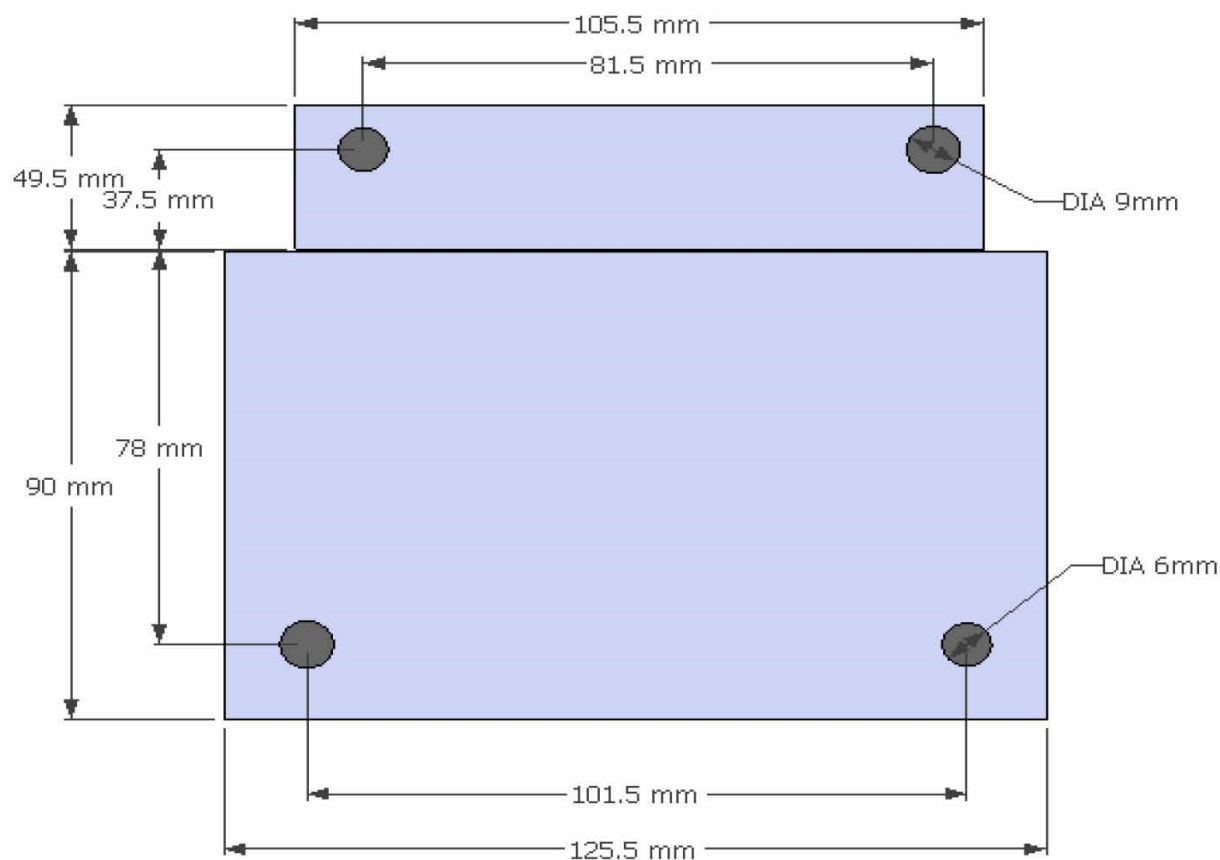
Montage lumière stroboscopique dimensions du support pour KX080-3
